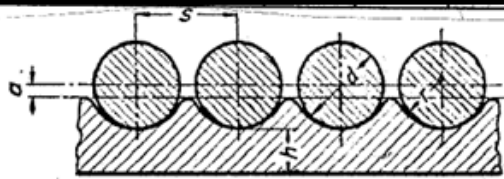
FIG. . — Dimensiones de las ranuras de los tambores de cables.
